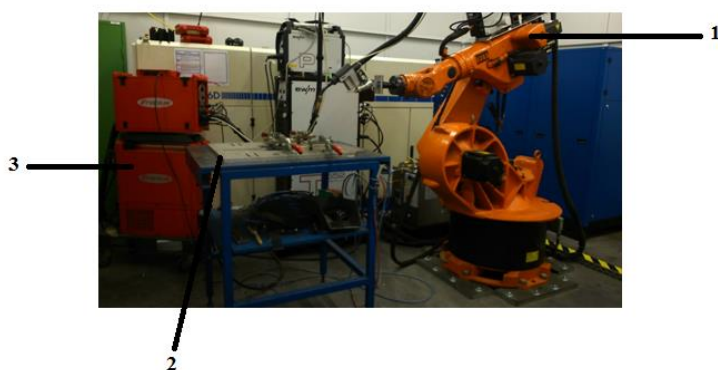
Сварочное оборудование СМТ, 1-сварочный робот «Кюка», 2-сварочный стол, 3-сварочная установка
